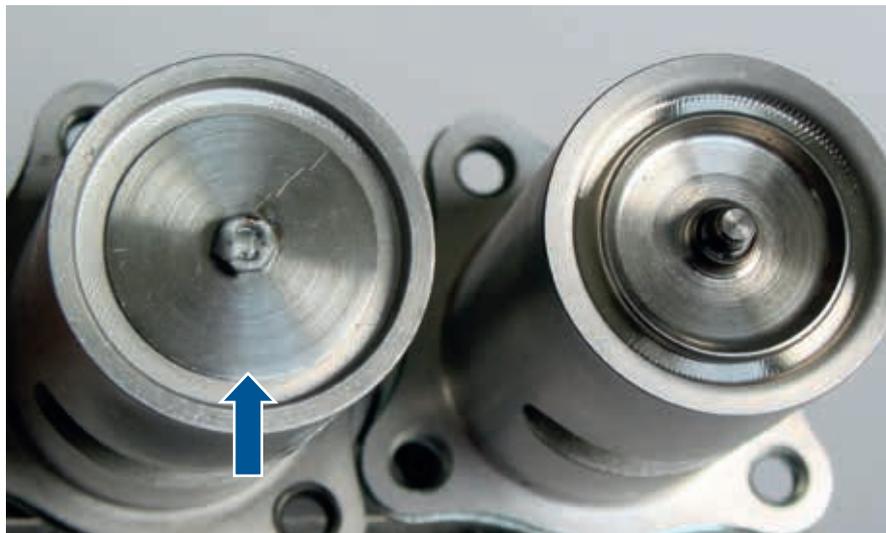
Eine angeschweißte Blechscheibe (Pfeil) ist kein Ersatz für einen Ventilsitz.
